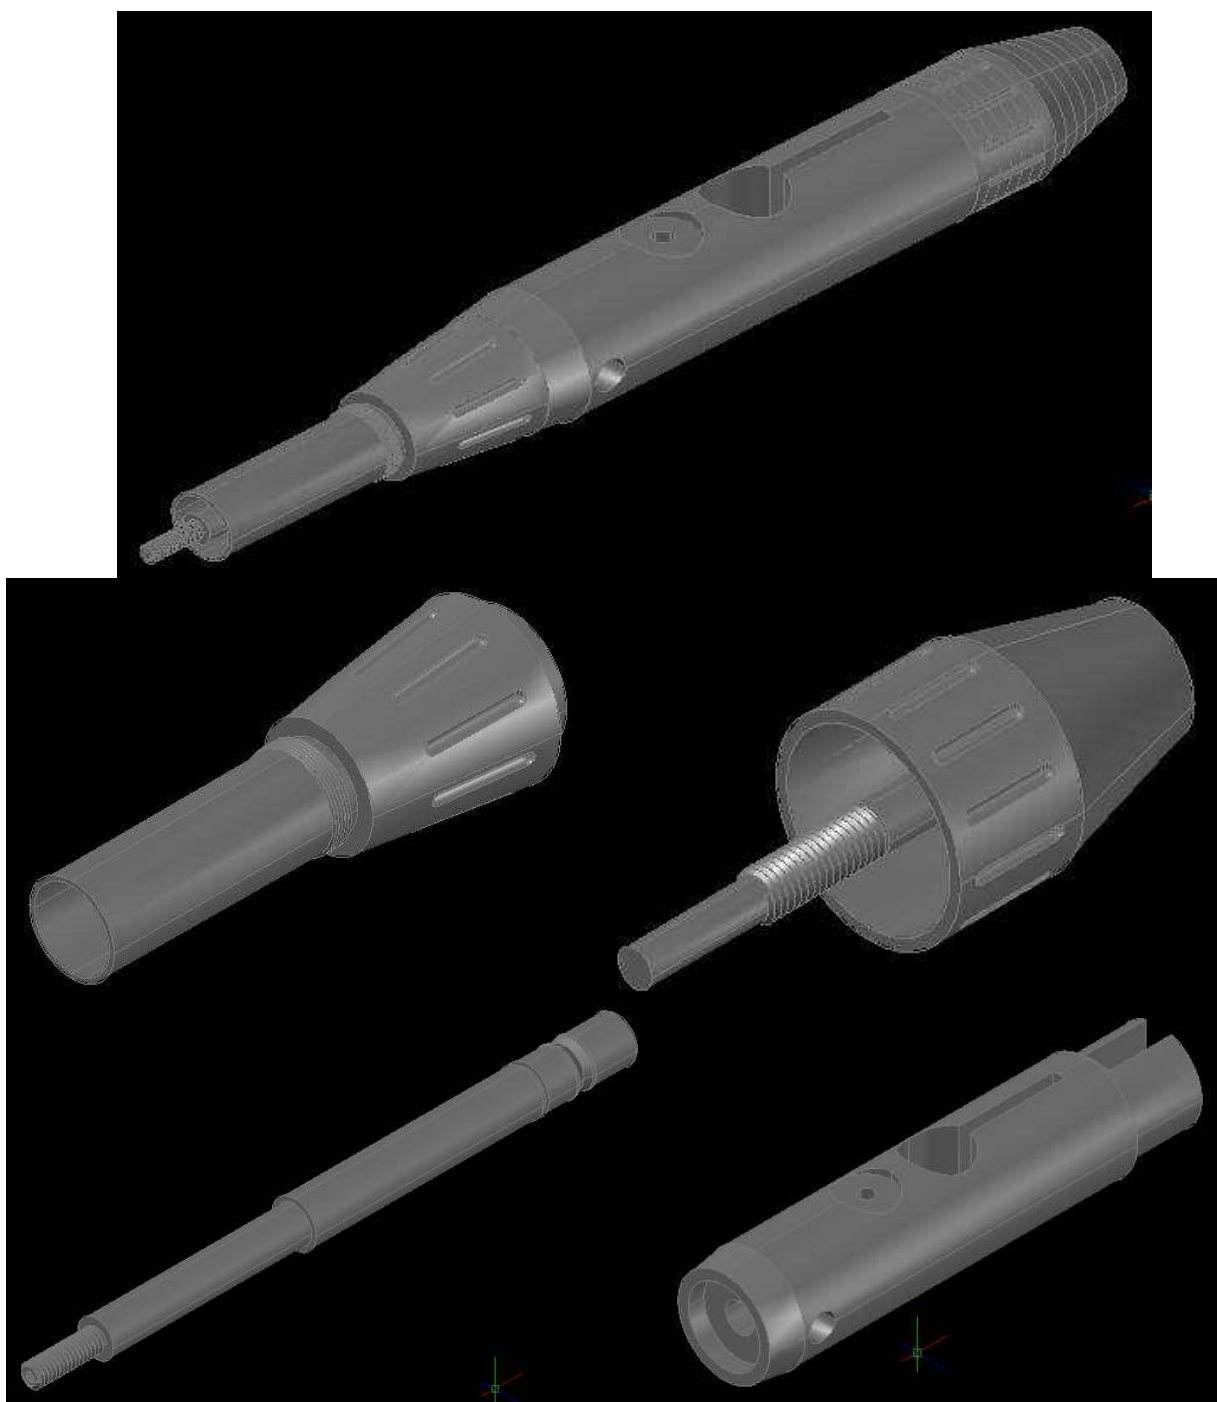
Dibujo en 3 dimensiones del Molinete Universal.
